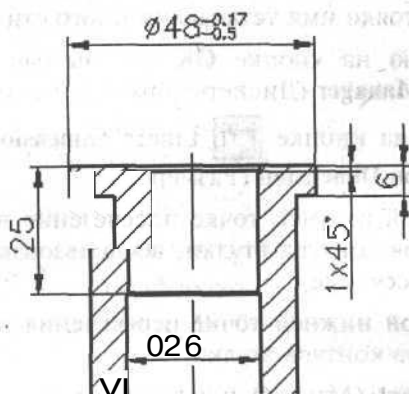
Чертеж втулки после нанесения линейного размера с допусками и знаком диаметра
